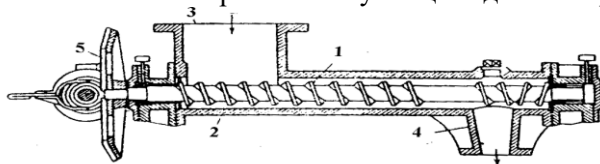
Шнековий затвор на лінії транспортування твердих подрібнених матеріалів: 1 – гвинт; 2 – корпус; 3 – завантажувальна воронка; 4 – патрубок для відповідної труби; 5 – зубчаста передача
